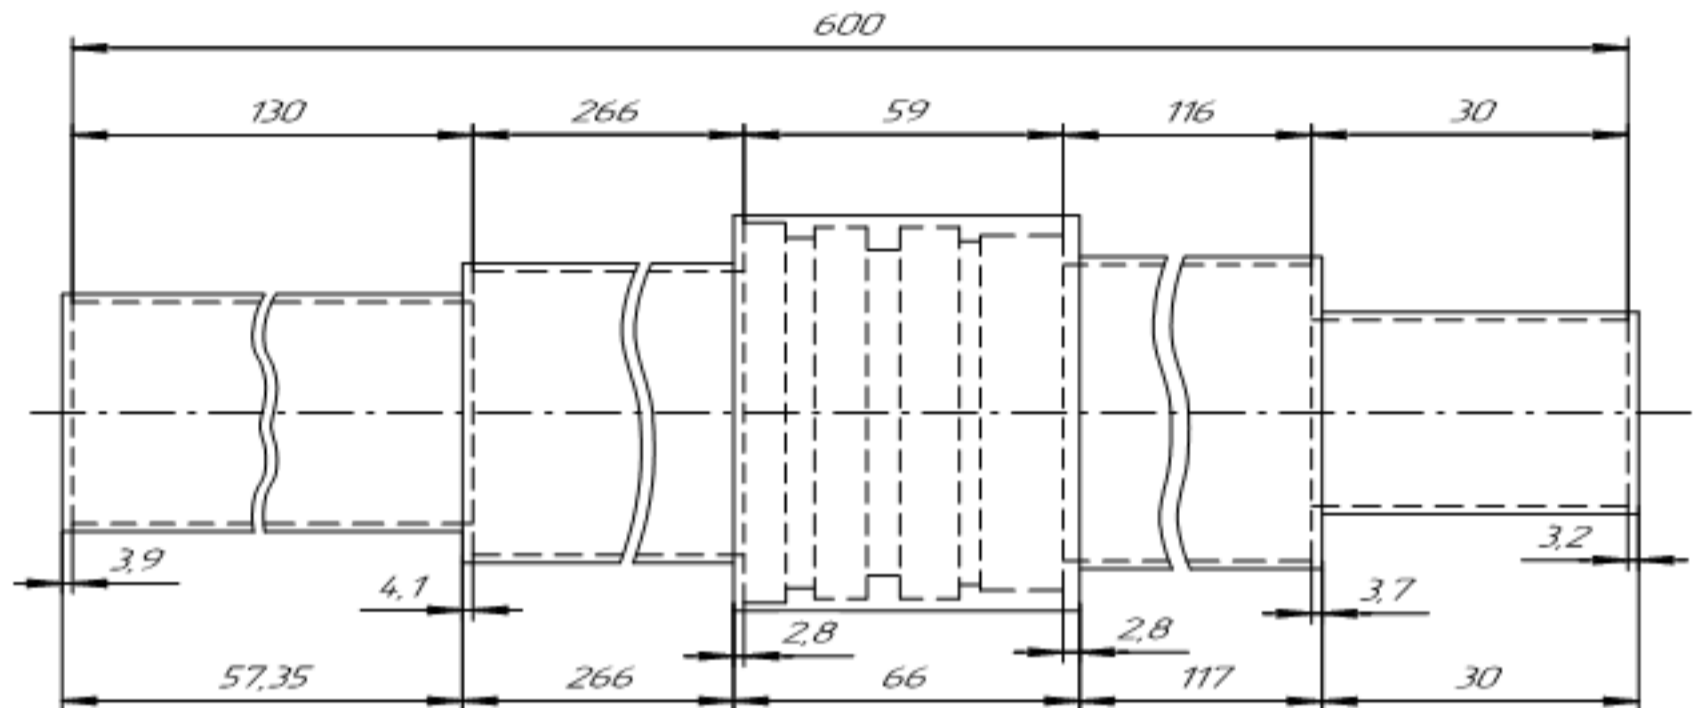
До визначення лінійних розмірів заготовки
